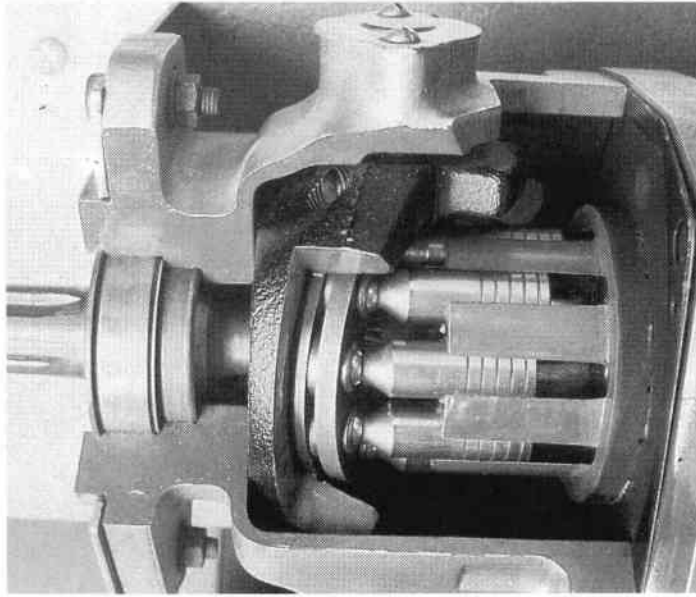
Vue d'une pompe hydraulique à pistons axiaux et plateau inclinable Vickers
